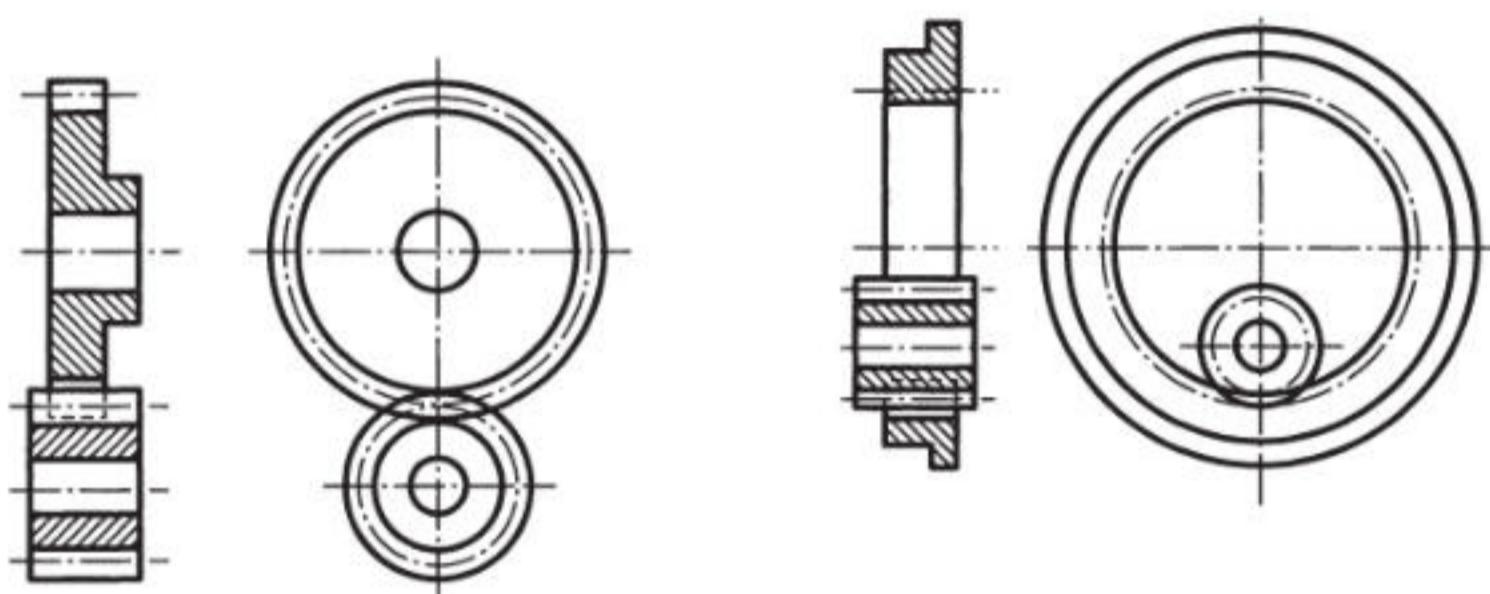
Условное изображение зубчатых передач с цилиндрическими колесами
